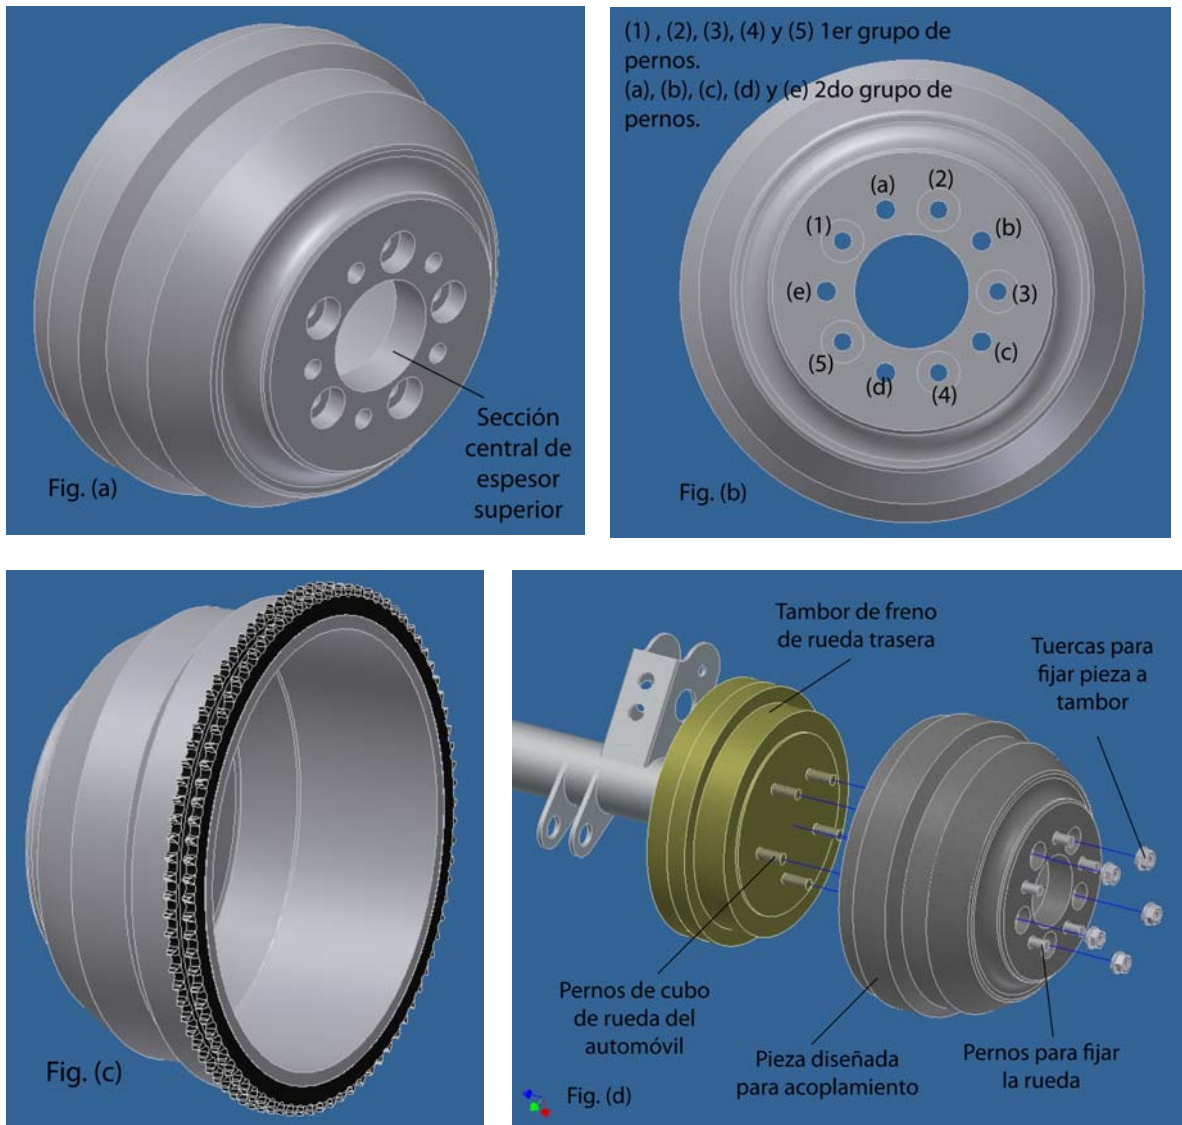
Pieza de acoplamiento entre rueda dentada y cubo de rueda: (a) Vista en isometría, (b) Vista frontal, (c) Ensamble con rueda dentada y (d) vista explosionada de ensamble con tambor de freno.
